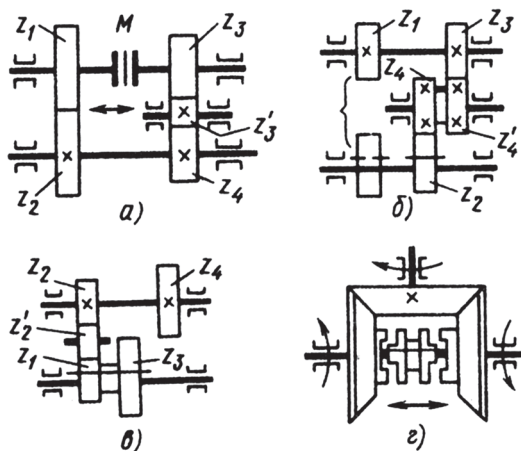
Кинематические схемы (а-г) реверсивных механизмов
